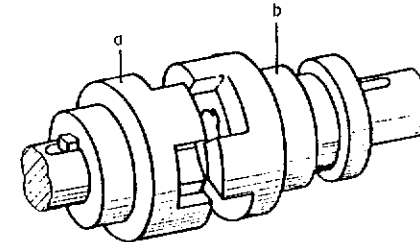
Acoplamiento de garras. a) Parte del acoplamiento enchavetada de modo fijo al extremo izquierdo del árbol; b) parte del acoplamiento deslizante en sentido longitudinal a lo largo del extremo derecho del árbol.
